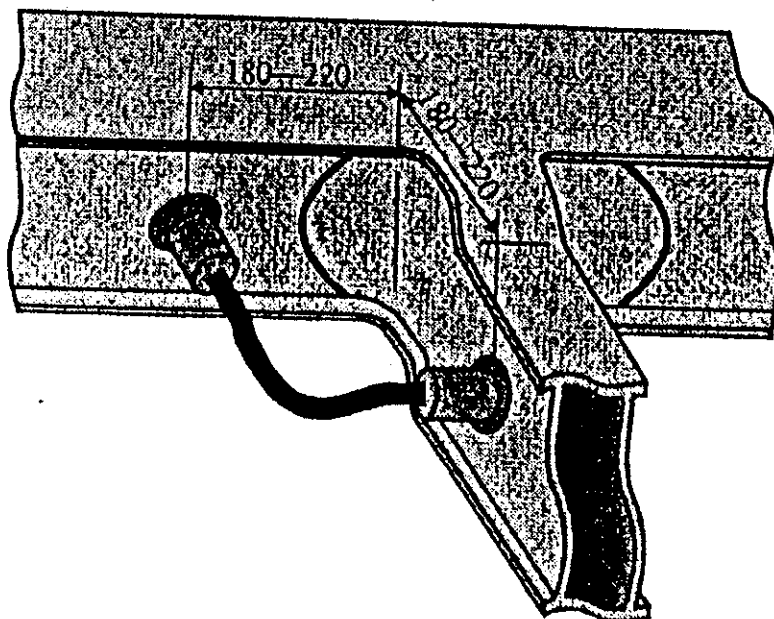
Намагничивание перехода от продольной балки к поперечной
